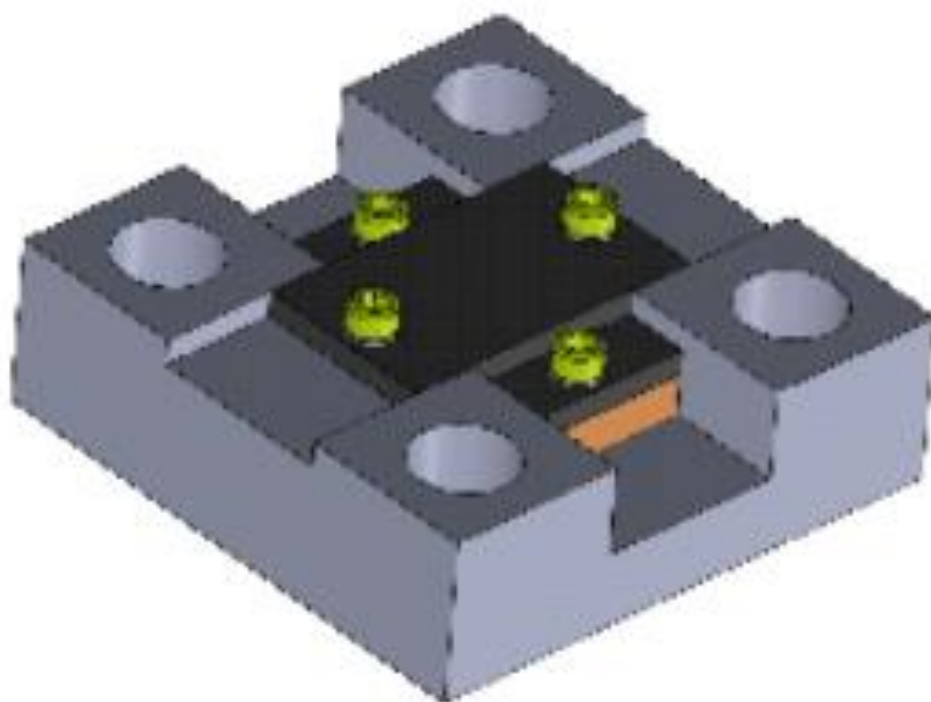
Оснастка для фиксации плоских образцов при сварке
